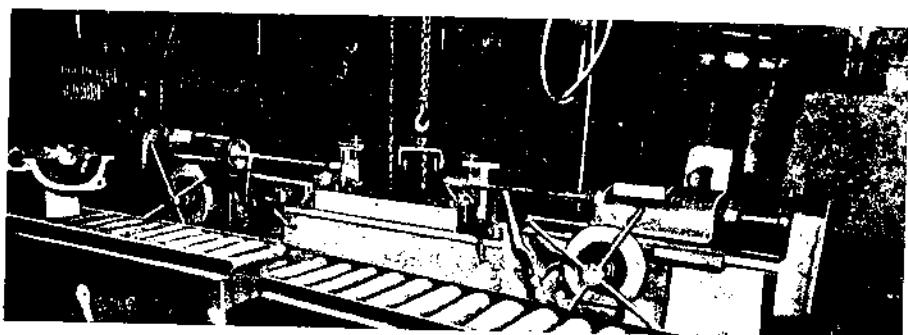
Станок Varnes для сверления центрального смазочного канала в блоке.
